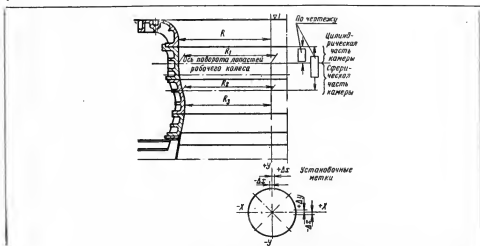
Проверка цилиндричности камеры рабочего колеса.
